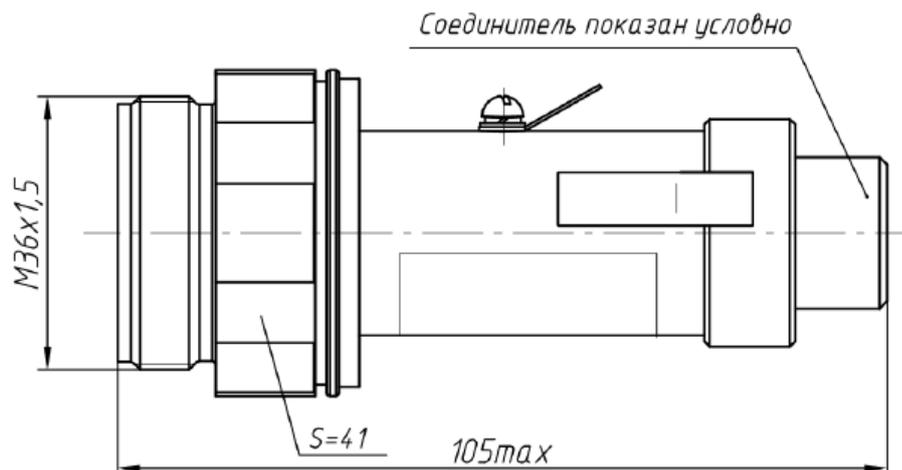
Габаритный чертеж преобразователей гидростатического давления с кодом присоединительного размера 2 и кодом конструктивного исполнения К00
